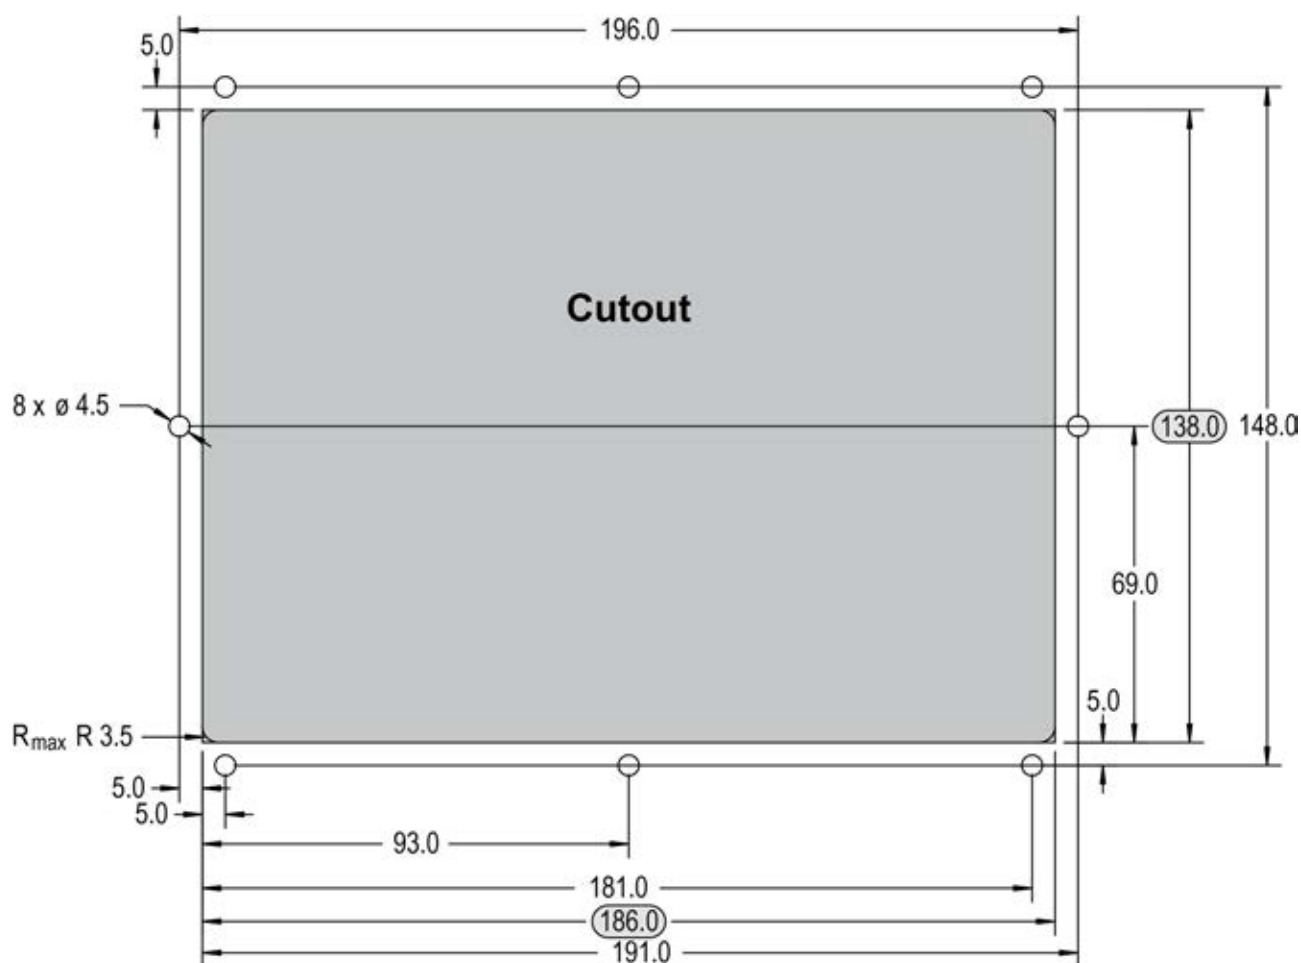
Пластмассовый корпус - план просверливания отверстий
